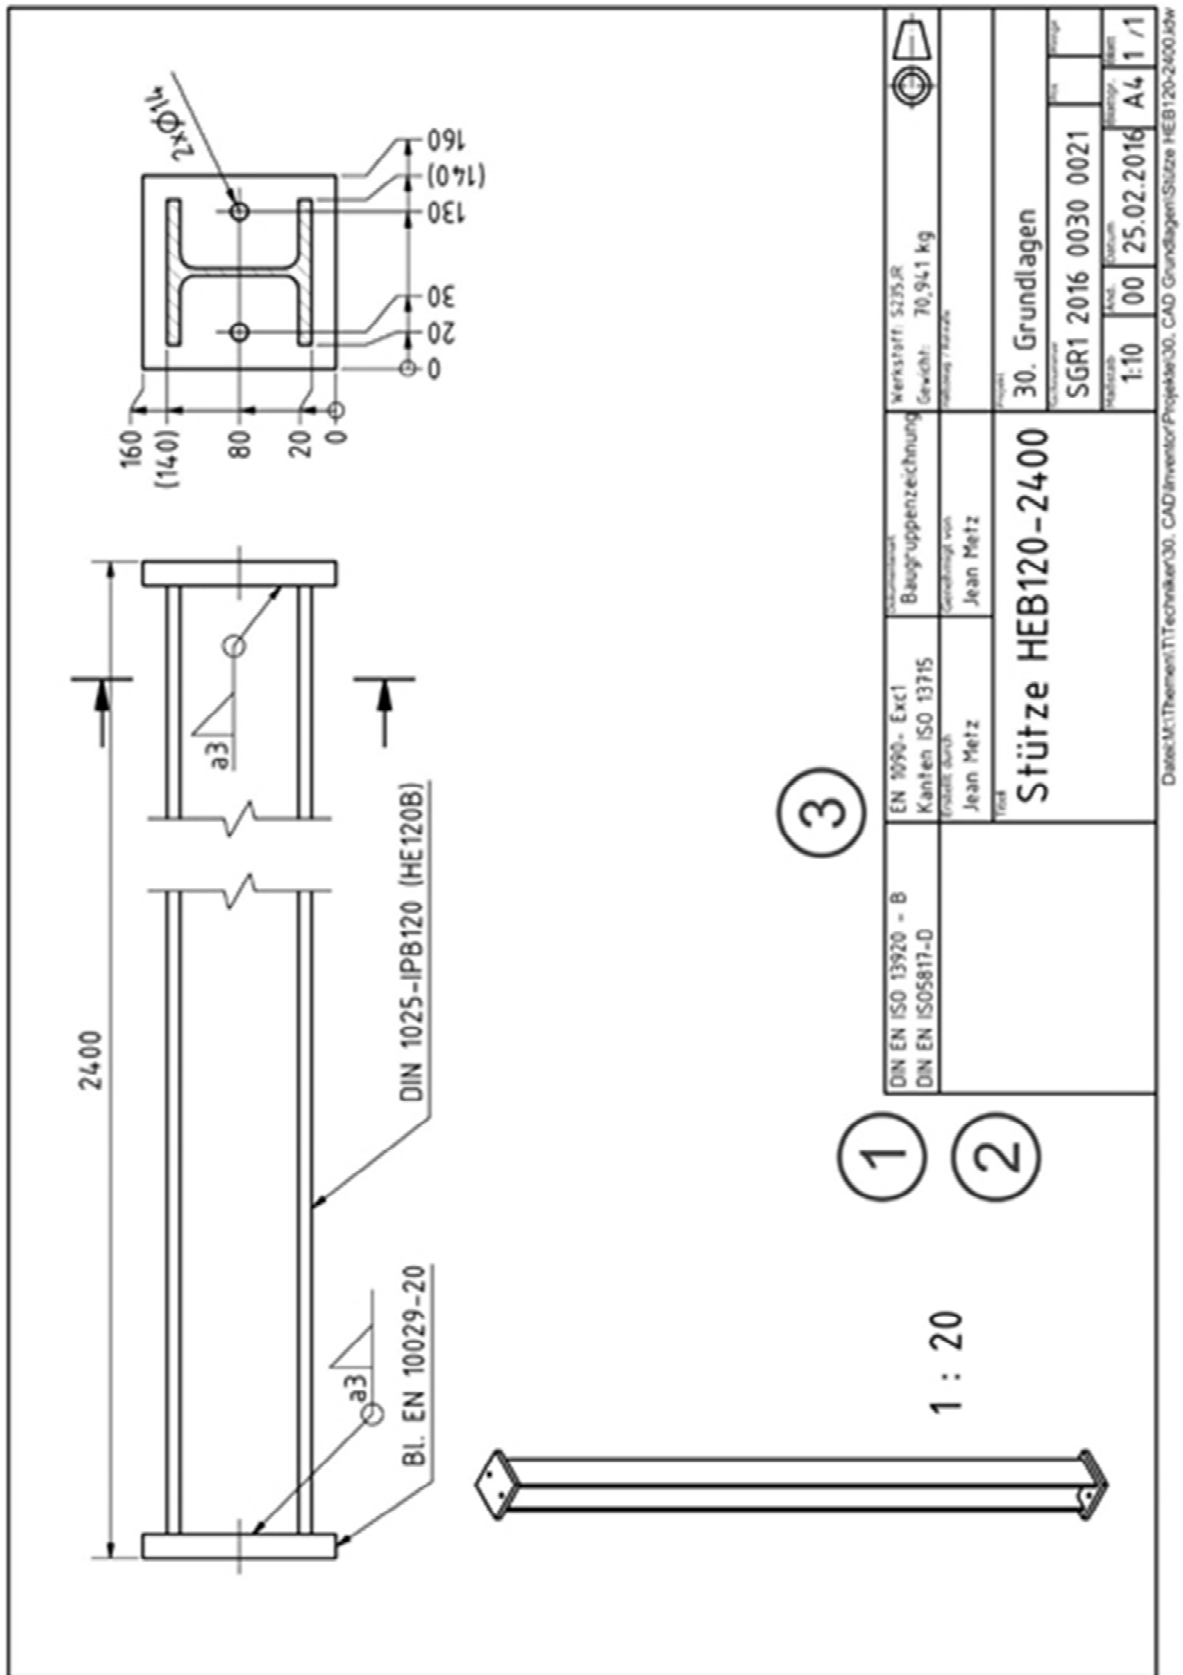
Зварювальний креслик «Підтримка НЕВ 120-2400»
